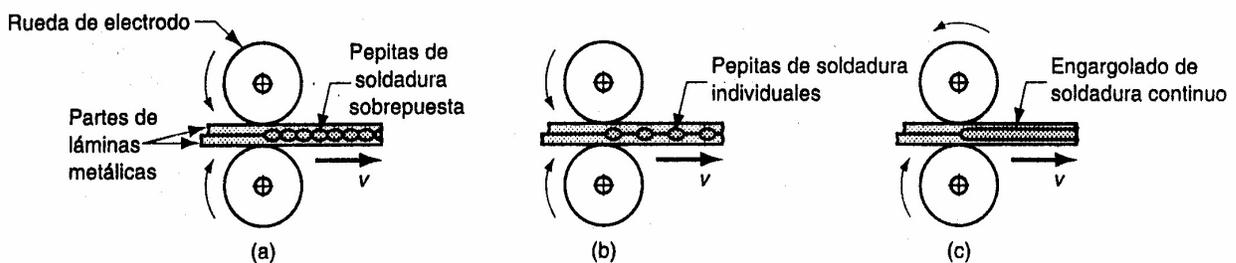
Diferentes tipos de engargolados producidos por ruedas de electrodos: (a) soldadura de engargolado por resistencia convencional, en la cual se producen puntos sobre puestos, (b) soldadura de puntos en rollo y (c) soldadura por resistencia continua
